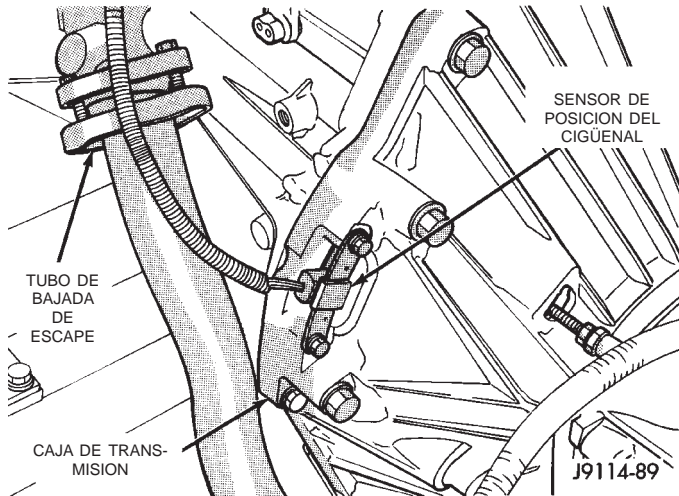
Sensor de posición del cigüeñal—Motor 2.5L
